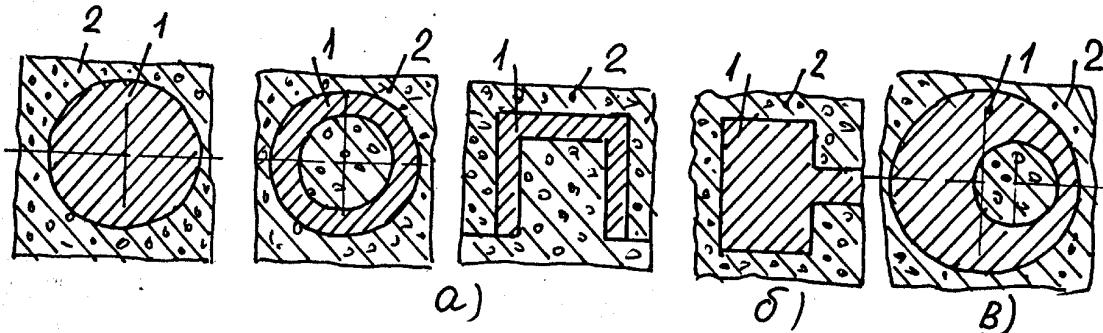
Схема торможения усадки: а)- механическое; б) тепловое; в) комбинированное. 1- отливка 2- форма.
